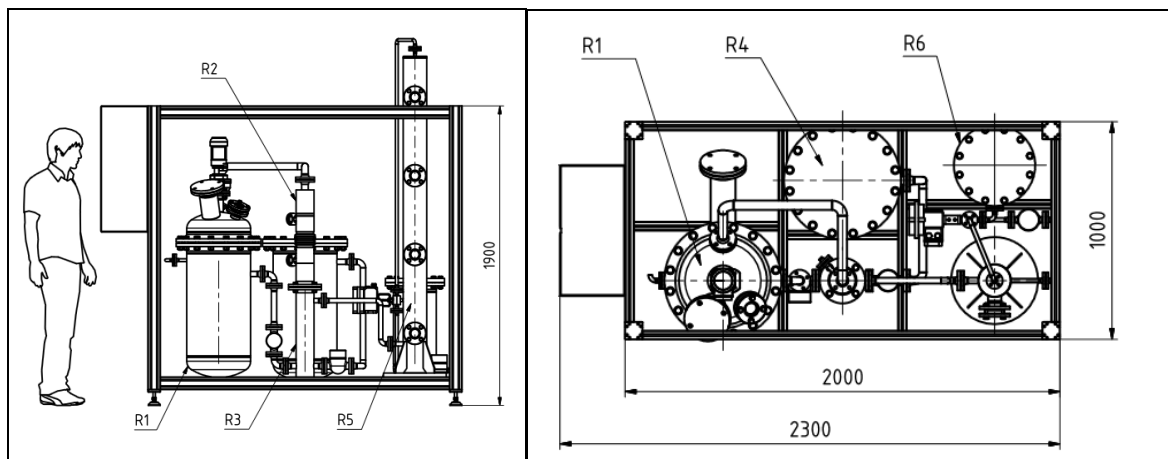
Übersichtszeichnung Technikumsreaktor - Ansicht von der Seite
